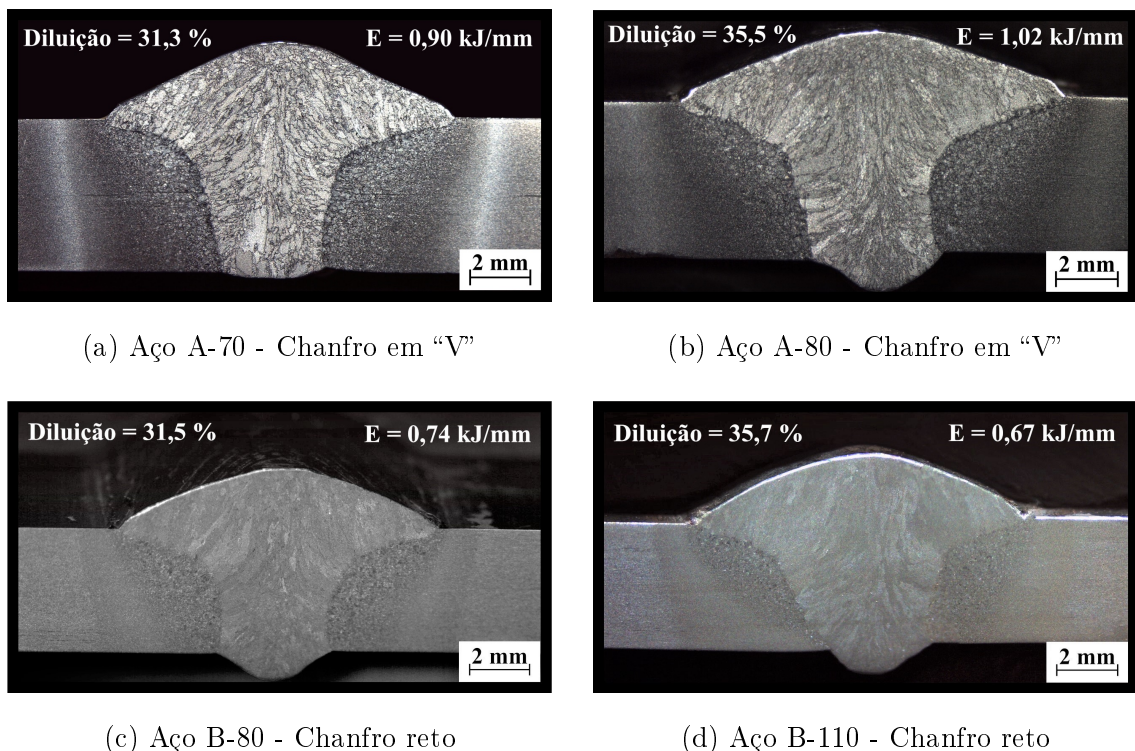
Macrografias dos cordões de solda para as quatro condições de soldagem.
